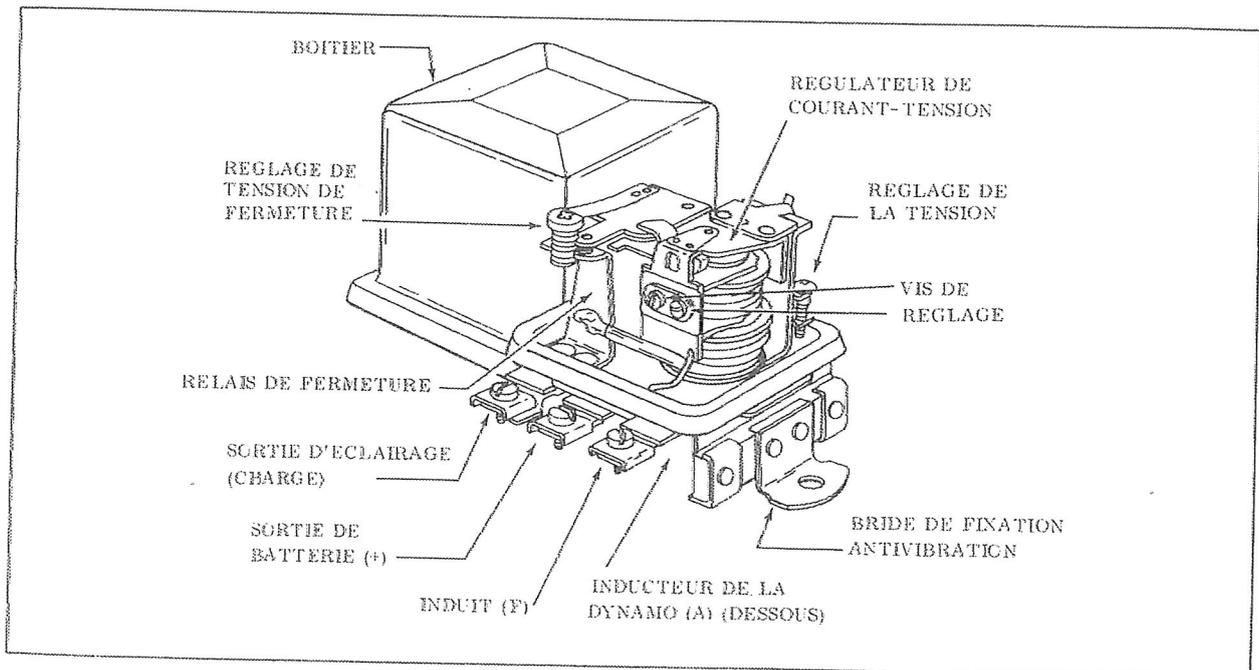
ENSEMBLE REGULATEUR DE TENSION
